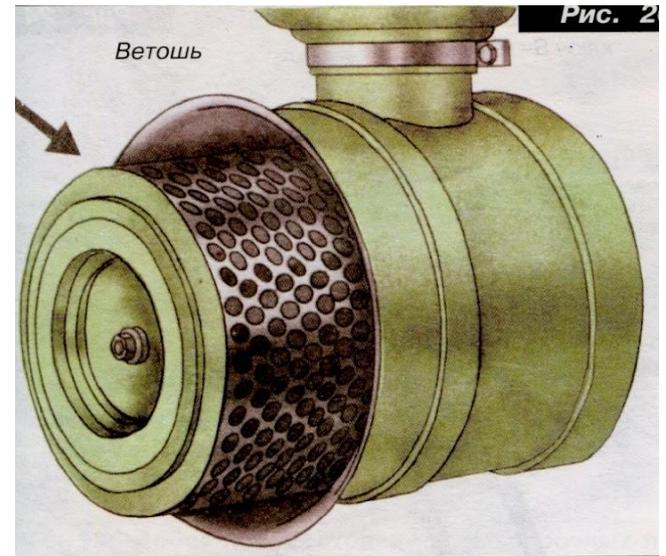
Сменить фильтрующий элемент воздухоочистителя.
